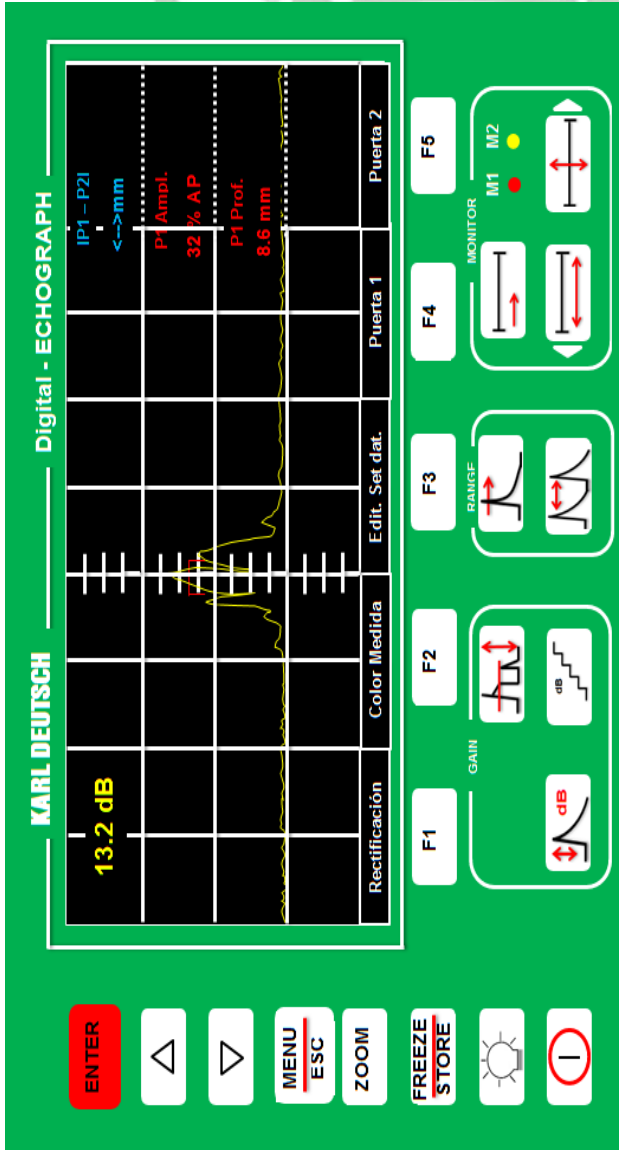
Pantalla de Inspección 1 lado derecho
